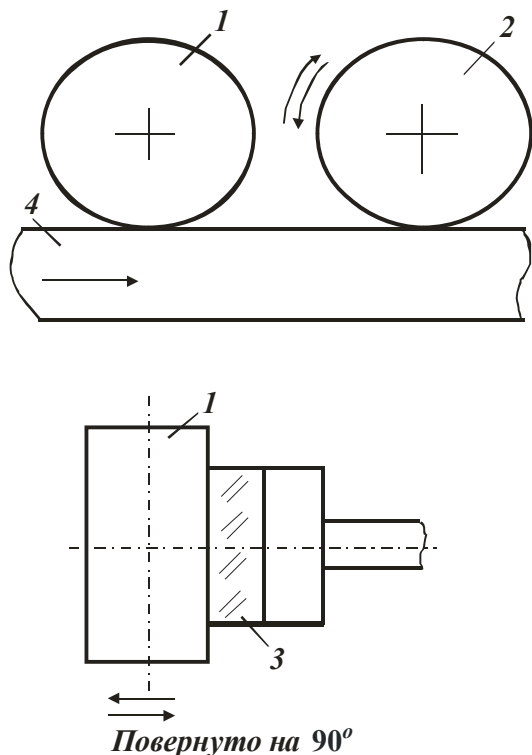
Схема обкатки при абразивно-шлифовальной обработке: 1 – обкаточный круг; 2 – шлифовальный круг; 3 – вибратор, приводящий в движение обкаточный круг; 4 – обрабатываемая деталь.
